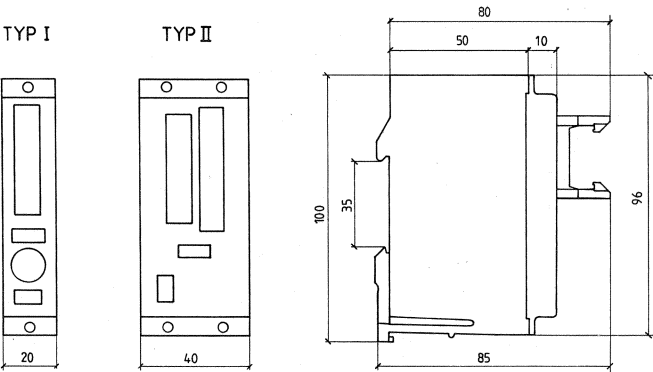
Anpassungsblöcke für Zeit-/Zählerbaugruppe 381
